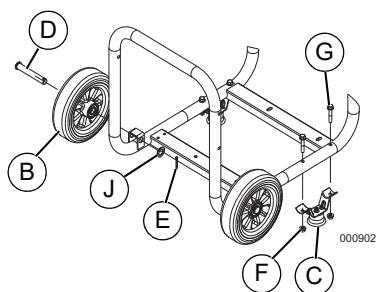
Ensamblaje de las ruedas y las patas de la estructura
